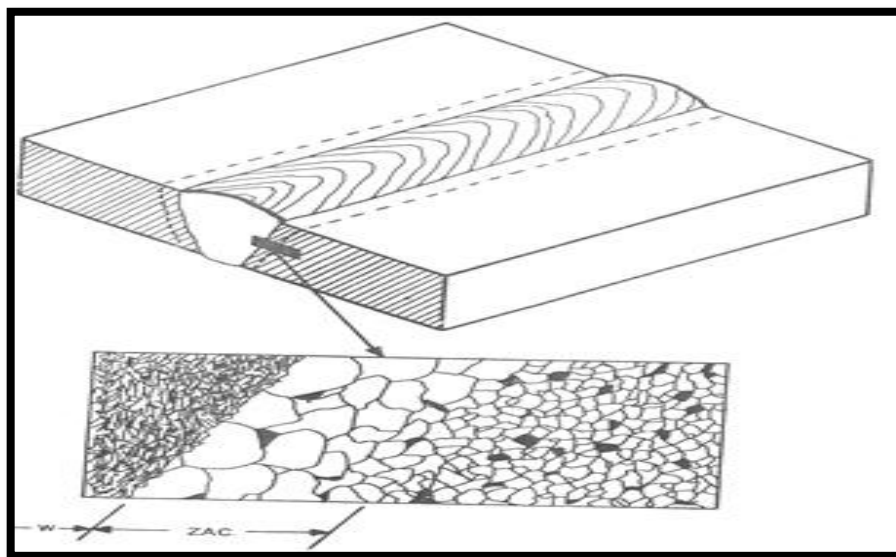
Diagrama de soldadura en una plancha de acero
